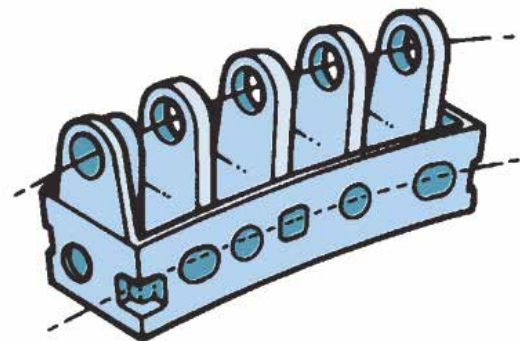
Деформация головки цилиндров с верхним расположением распределительного вала. Если поверхность головки цилиндра, сопрягаемую с прокладкой, механически обработать, придав ей плоскую форму, подшипники распределительного вала не получат надлежащего выравнивания. Расточите отверстия под подшипники распределительного вала для выравнивания отверстий тоннеля распределительного вала; источник: *Pearson Education, Inc.
